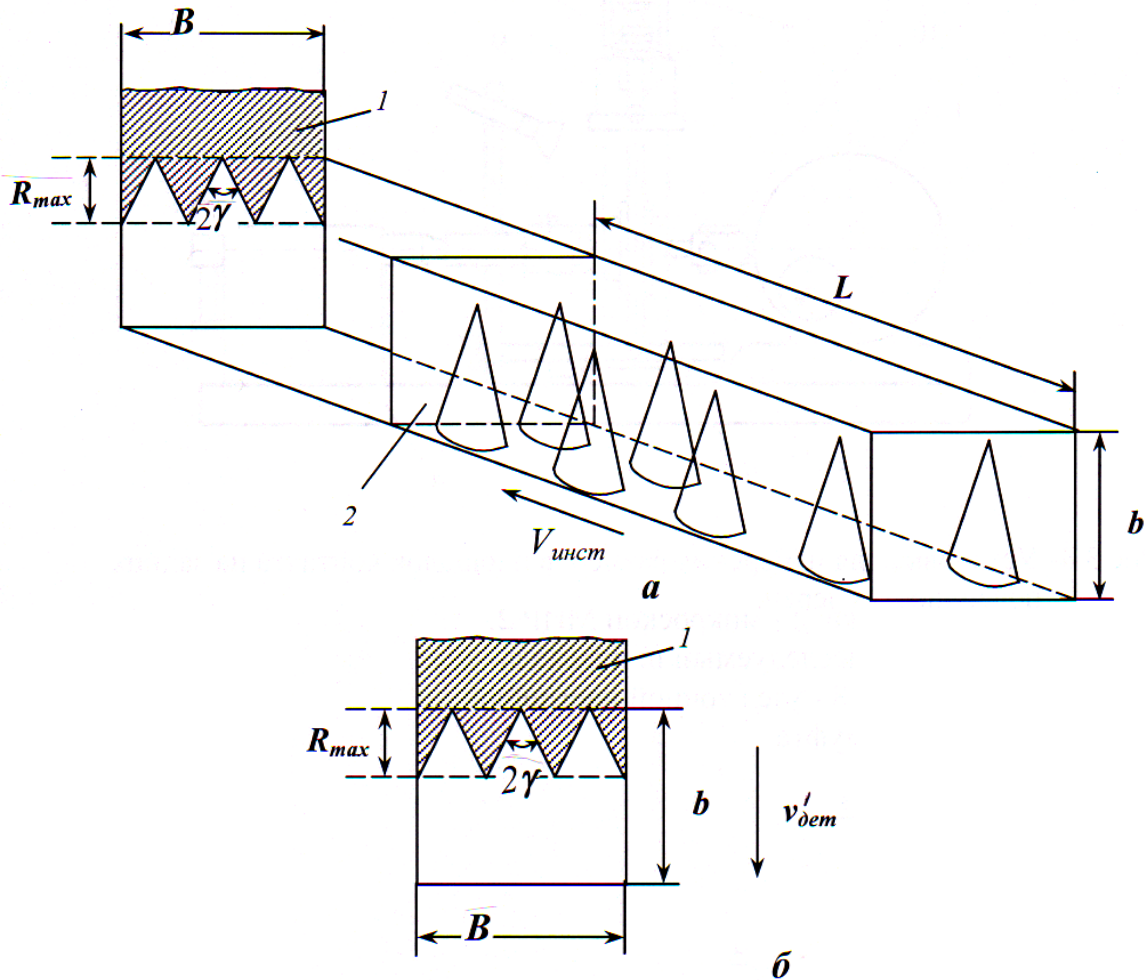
Расчетная схема: 1 – обрабатываемая деталь; 2 – абразивный инструмент.
